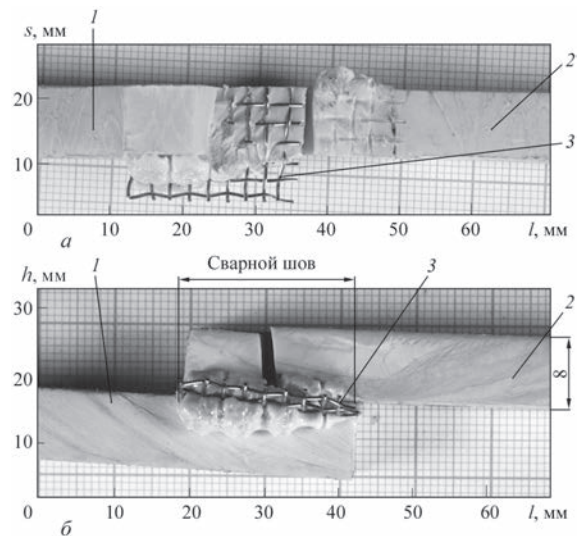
Характер разрушения образца (l — длина, h — высота, s — ширина), вырезанного из равнопрочного нахлесточного сварного соединения полимерного материала ZX-410: a — вид сверху; b — вид сбоку (1 — образец 2; 2 — образец 1; 3 — закладной элемент)
